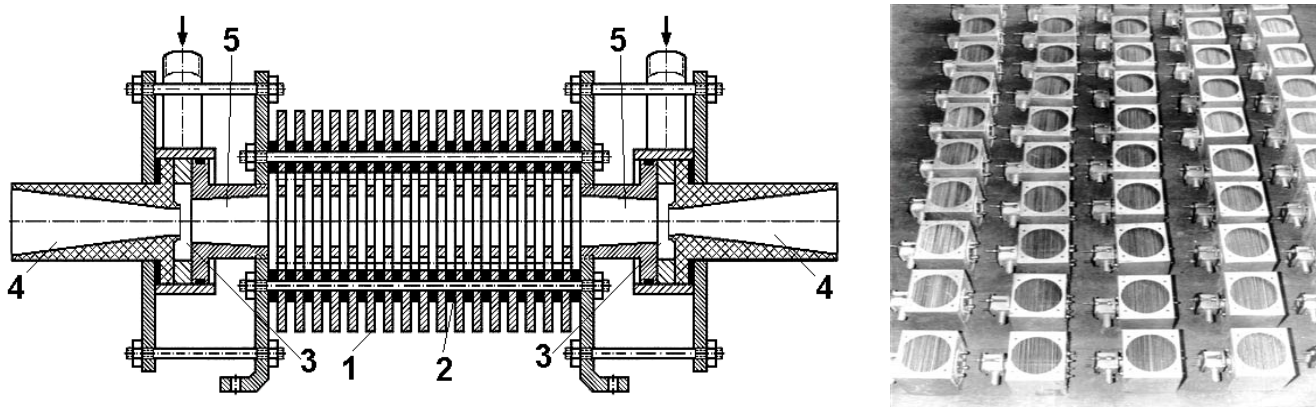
Первые в мире промышленные неадиабатные ВТ с пластинчатым оребрением вихревой камеры: слева – двухкамерная ВТ марки РВТК-38/2 для климатических камер: 1 – ребро; 2 – прокладка; 3 – улитка; 4 – диффузор холодного потока; 5 – неоребранный конический участок вихревой камеры; справа - серийные многоцелевые ВТ марки РВТК-16/1 на участке сборки готовой продукции - перед установкой вентилятора на кожух, охватывающий «горячее» оребрение вихревой камеры.
